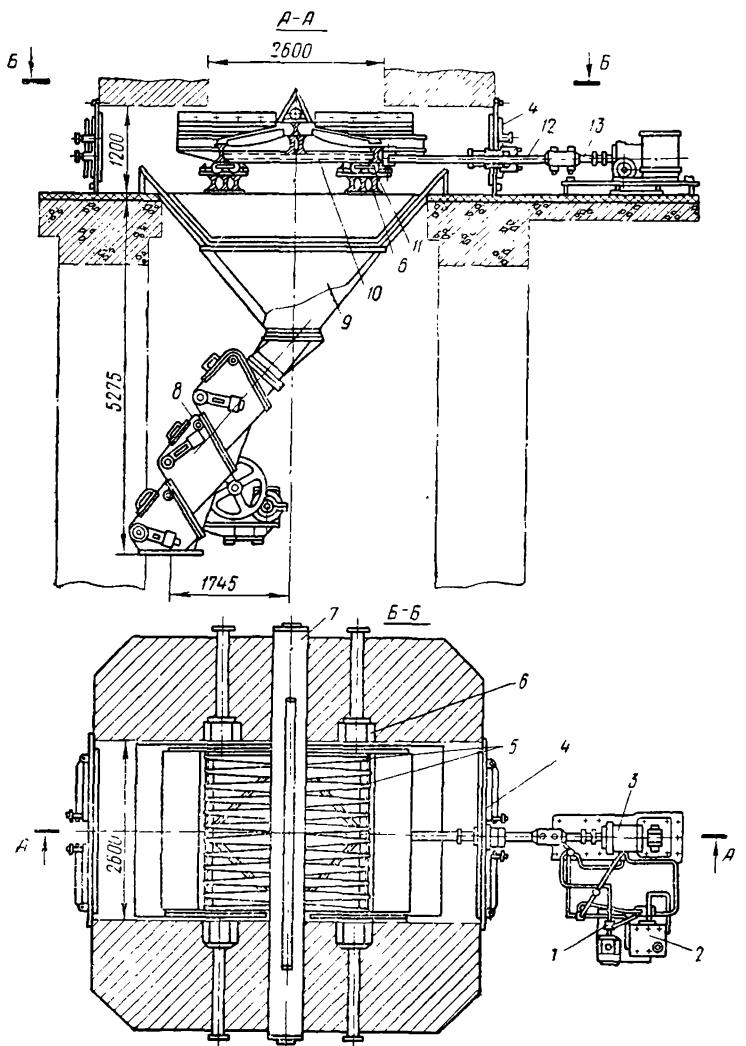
Выгрузочное устройство с движущейся решеткой конструкции Союзгипростроя:
